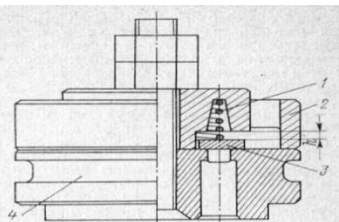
Клапан нагнетательный кольцевой пластинчатый четвертой ступени.
